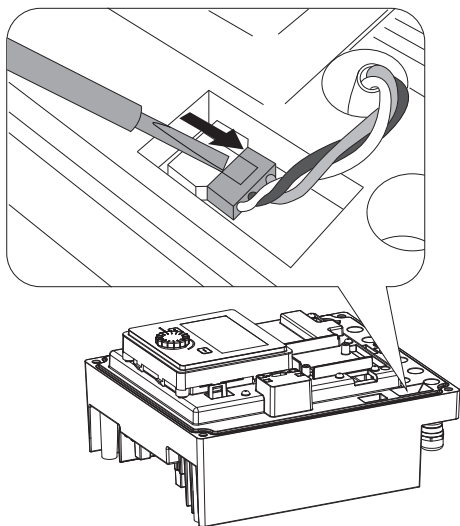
Soltar el cable de conexión del ventilador del módulo
